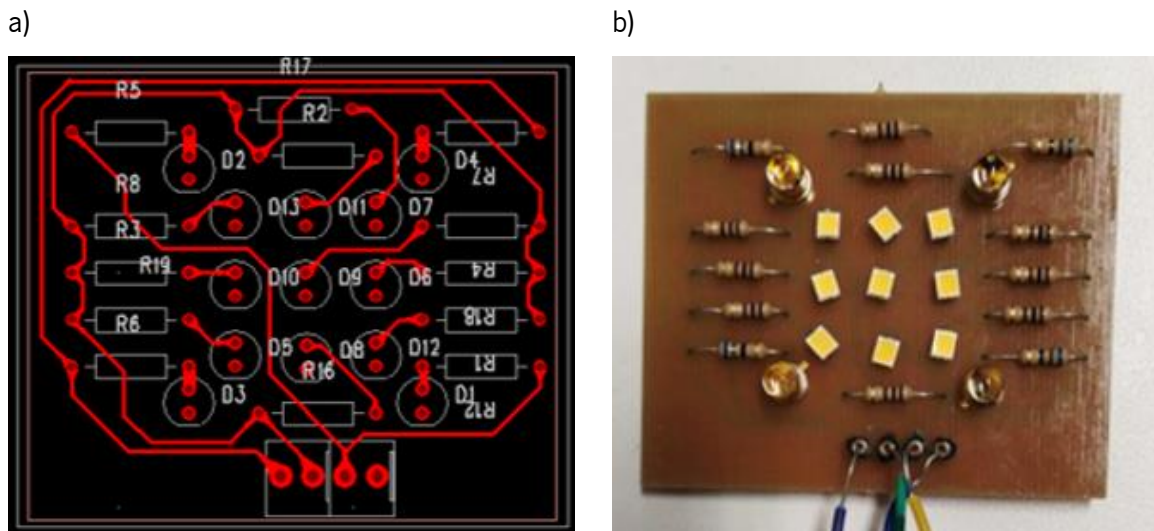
a) Layout da PCB desenhada com auxílio do programa PADS para a Placa de Emissão 1. b) Fotografia da placa desenvolvida.
